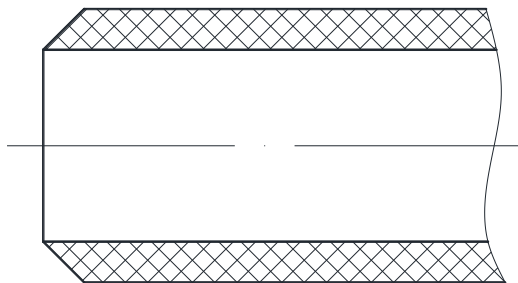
Конструктивные элементы шва сварного соединения (шов НС7)
